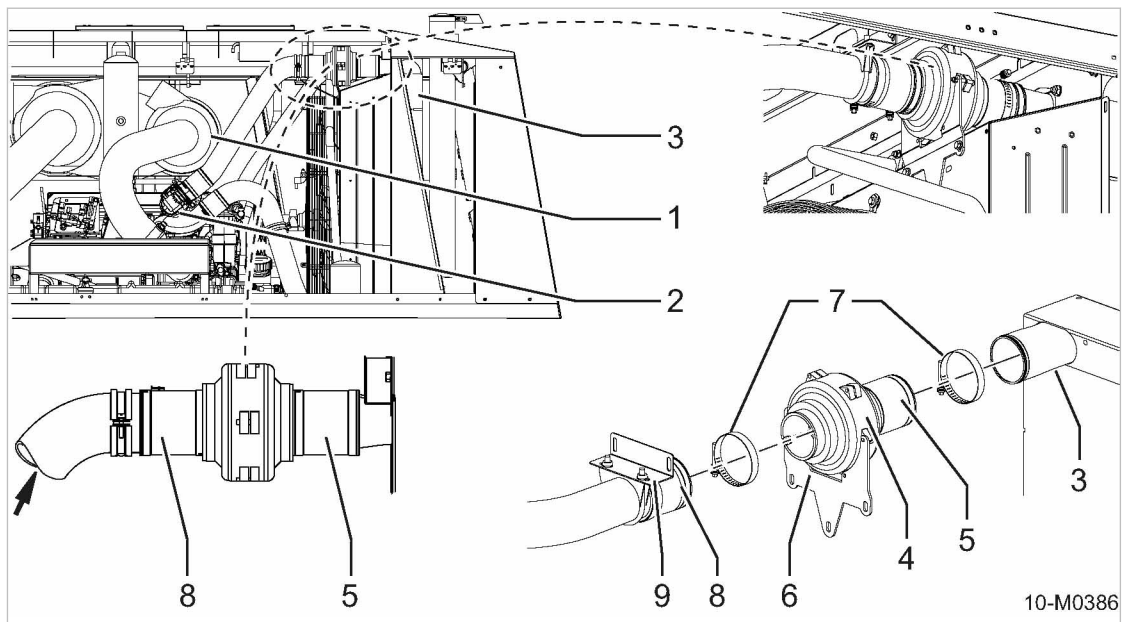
Mantenimiento de la válvula de cierre del aire del motor
